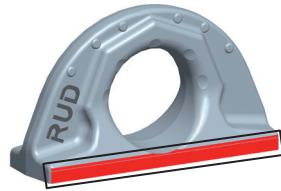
Zone de la jonction entre cordons de soudure
